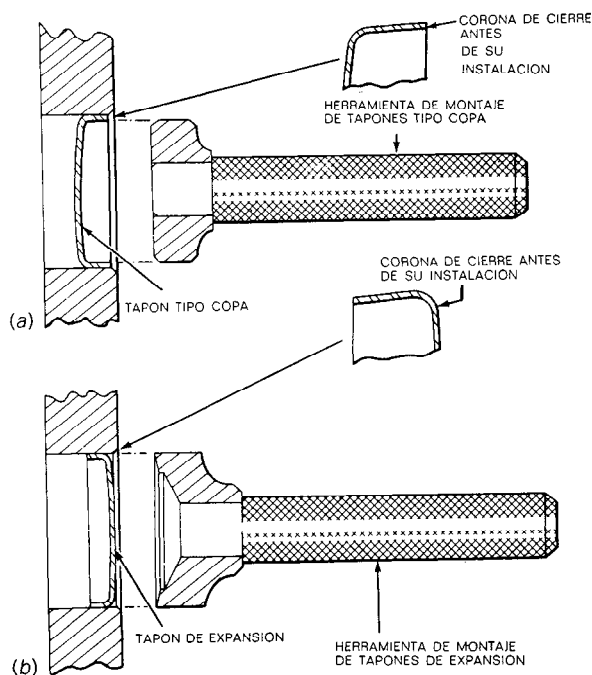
Tapones de expansión y herramientas de montaje (Ford Division of Ford Motor Company).
